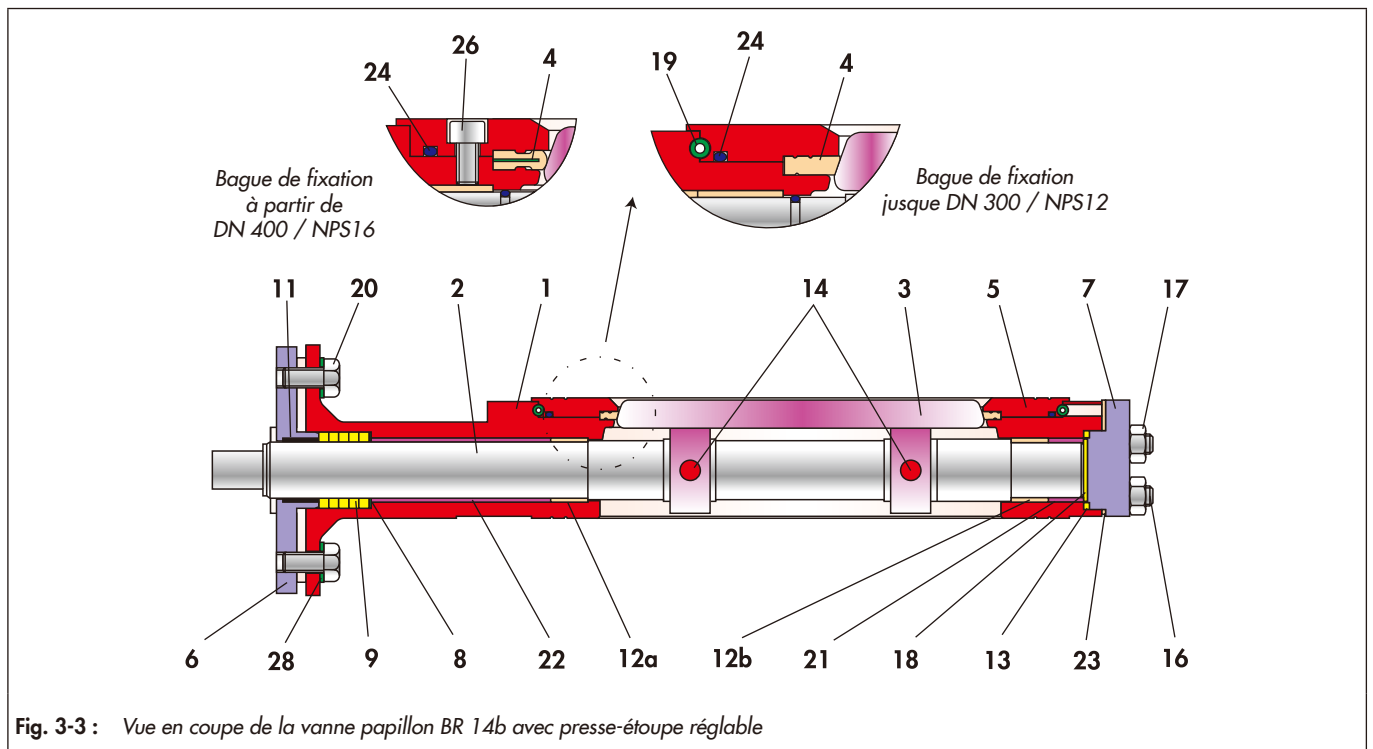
Vue en coupe de la vanne papillon BR 14b avec presse-étoupe réglable
